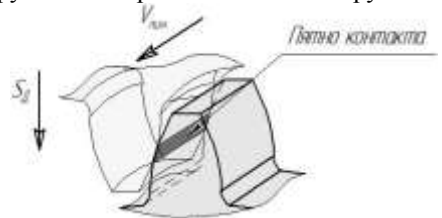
Схема касания поверхностей обрабатываемого зуба колеса и зуба притира
